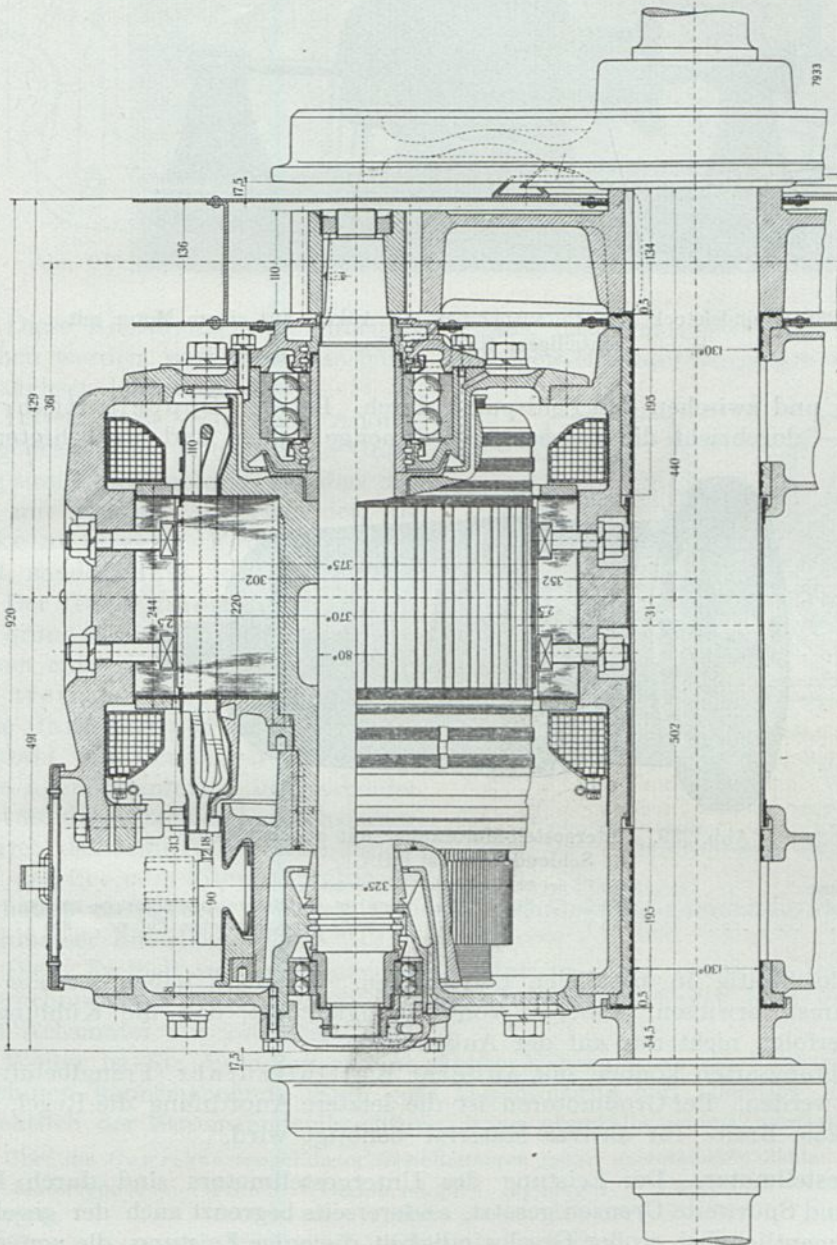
Längsschnitt durch einen Bahnmotor für Meterspur mit Kastengehäuse und Kugellager (B.B.C.).
